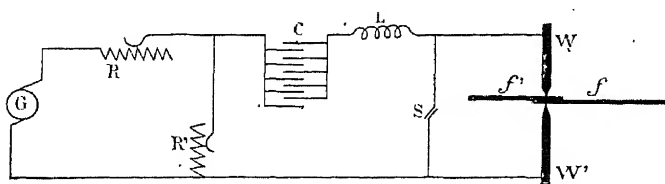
Soudure électrothermique des fils d'aluminium : dispositif de l'installation.
